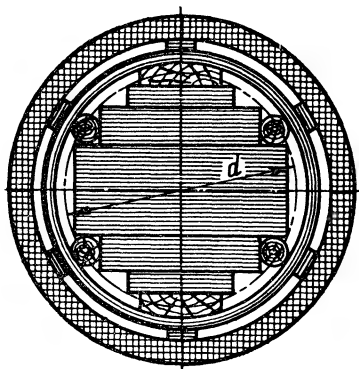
Прессовка стержня путем расклинивания с жестким бумажно-бакелитовым цилиндром обмотки НН.
